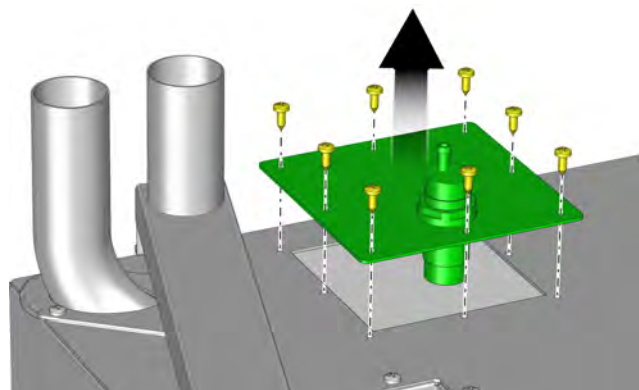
Chapa de montagem do sensor do nível de enchimento
